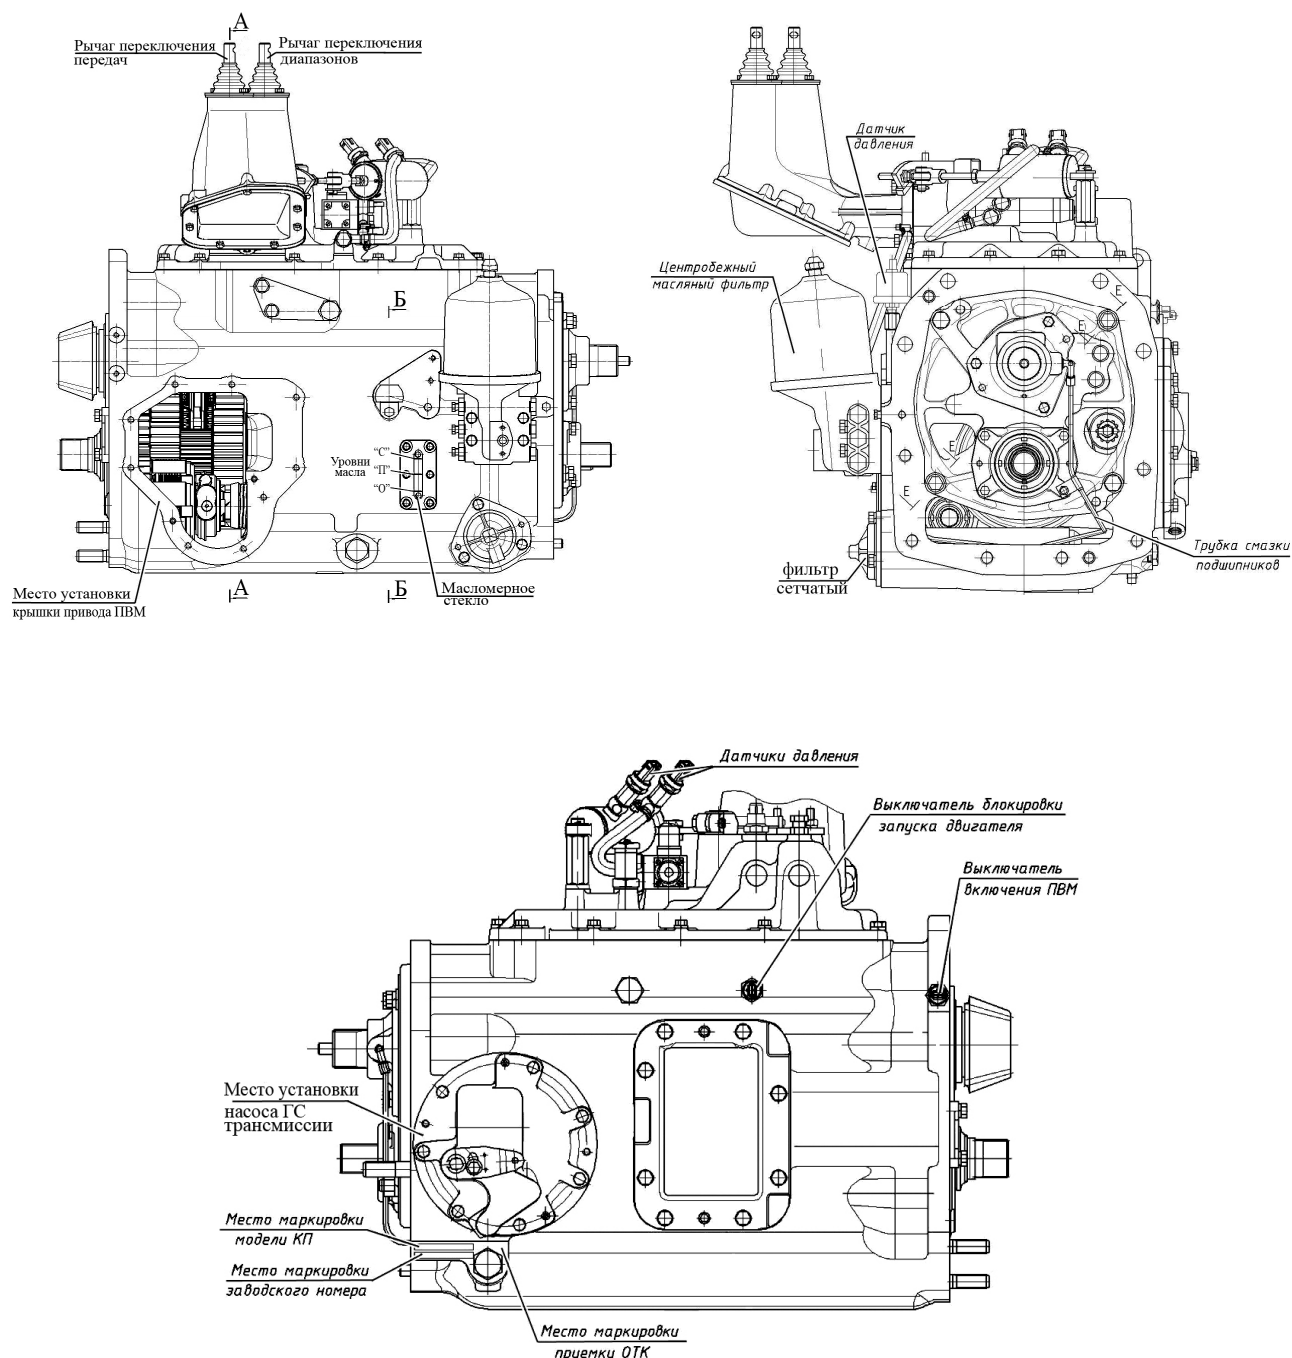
Внешний вид коробки передач (сечения А-А и Б-Б показаны на рисунке 3.3.2)
